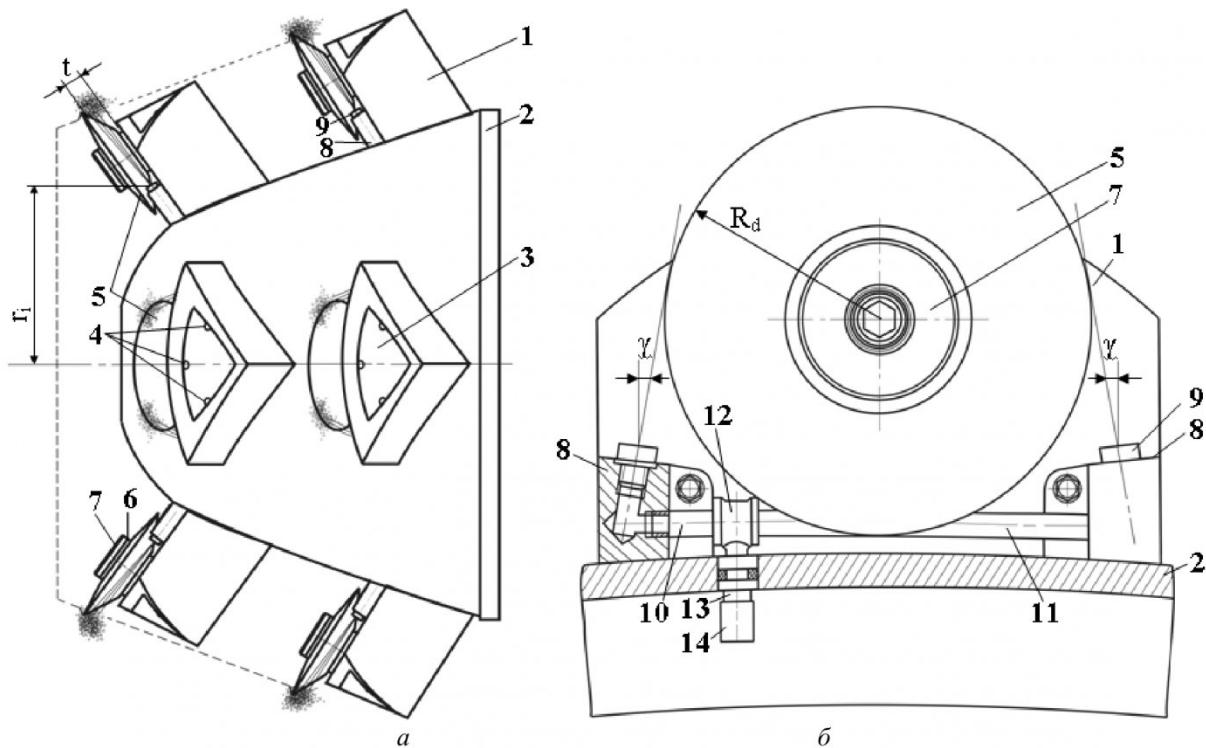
Реверсивная коронка проходческого комбайна с дисковым инструментом:
